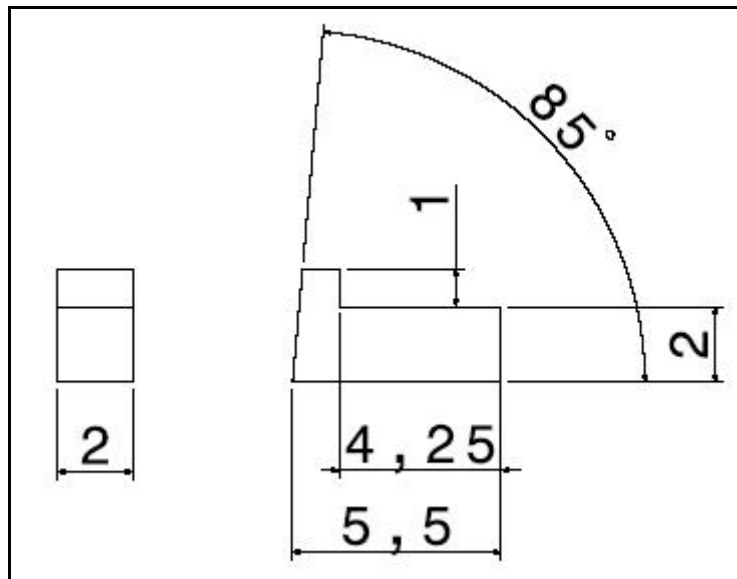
Dimensões da chaveta de cunha com cabeça.
